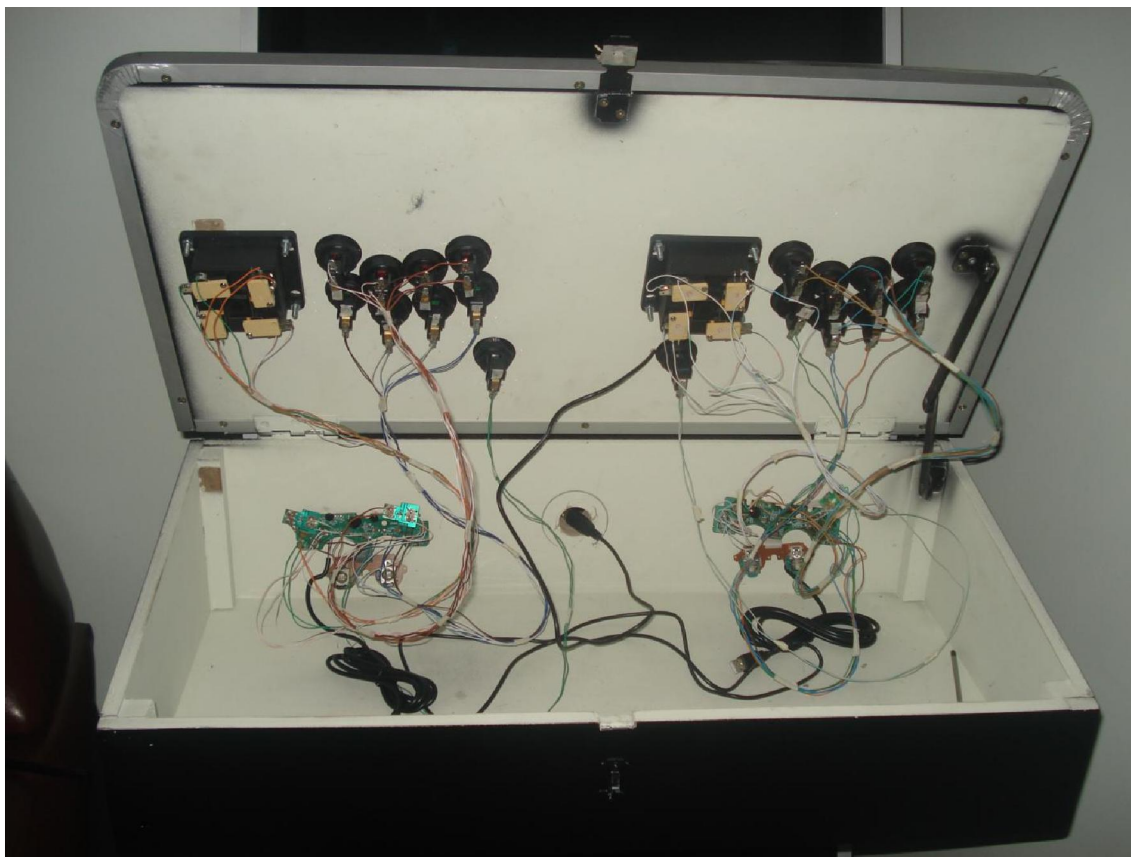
Controle já fixado no gabinete com os kits arcade soldados nas placas
